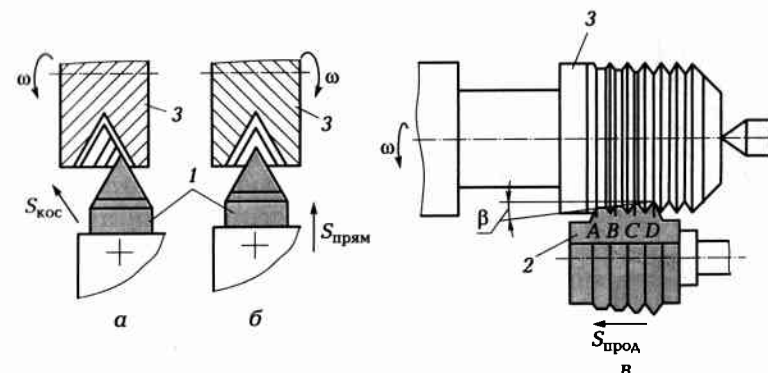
Схема нарезания метрической резьбы: а — резцом с косой подачей; б — резцом с прямой подачей; в — гребенкой
